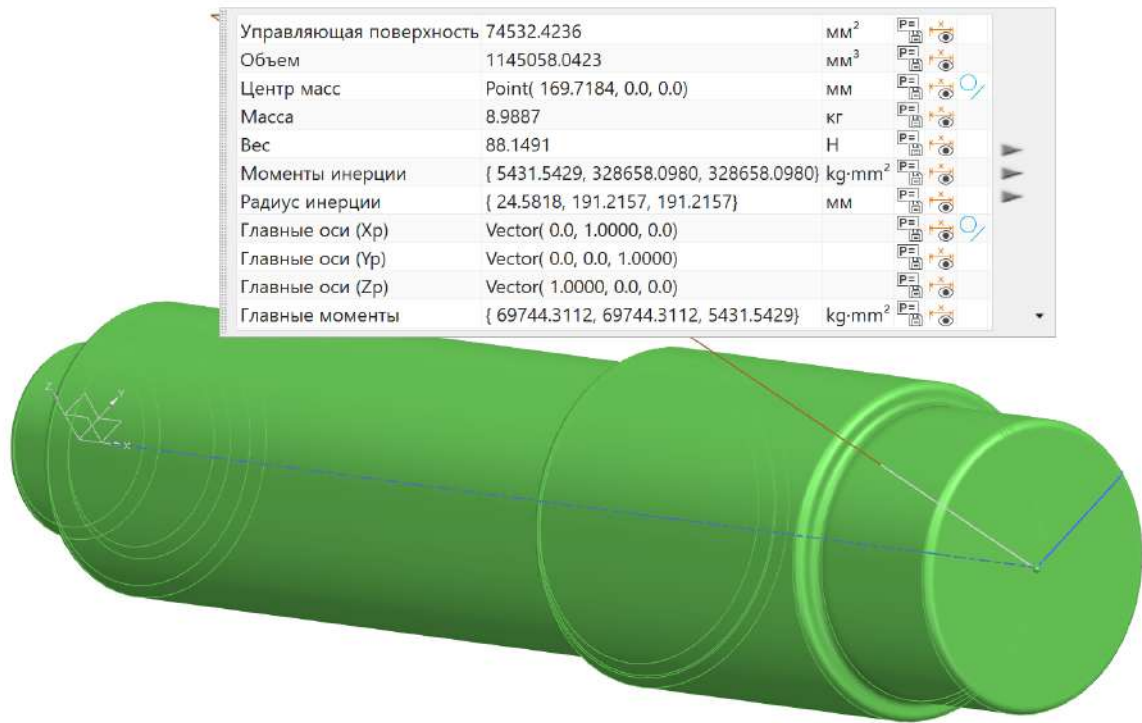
Тривимірна модель заготовки, що отримана поперечно клинковою прокаткою
